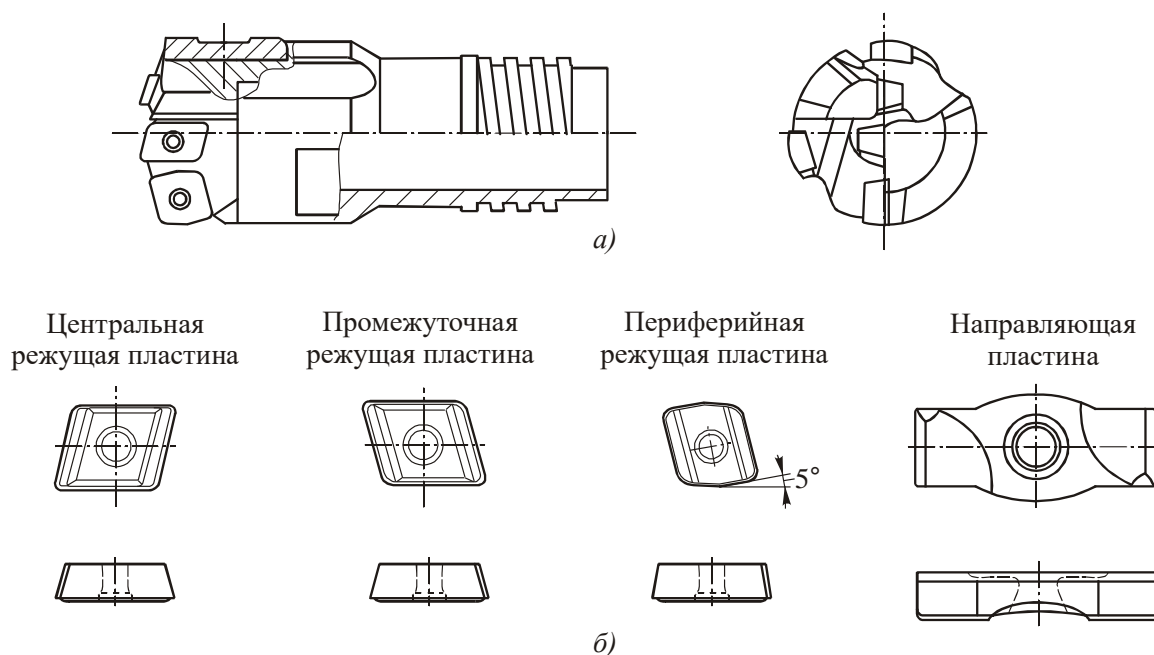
Сборная сверлильная головка БТА CoroDrill 800
